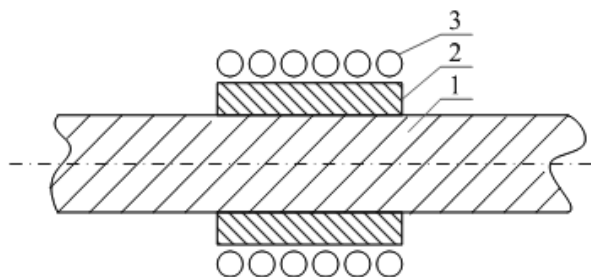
Пристрій для демонтажу деталей індукційним нагрівом: 1 – вал; 2 – втулка; 3 – обмотка індуктора
